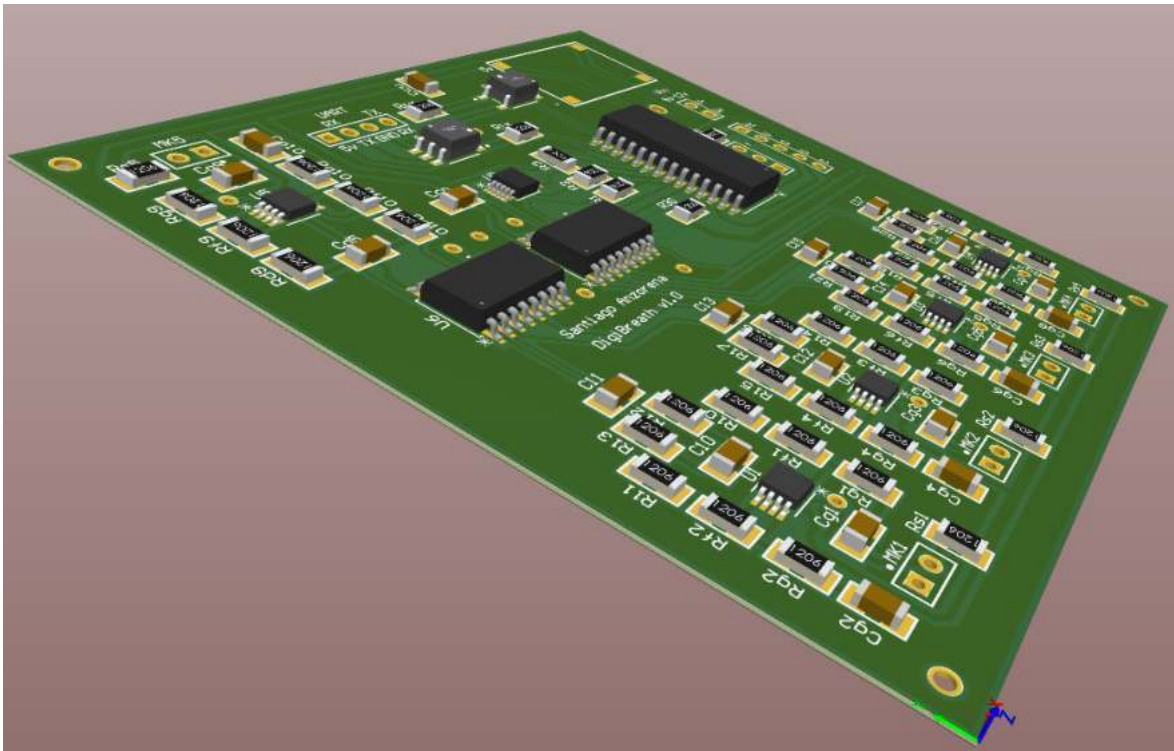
Diseño final de la placa en 3D. Vista isométrica.
